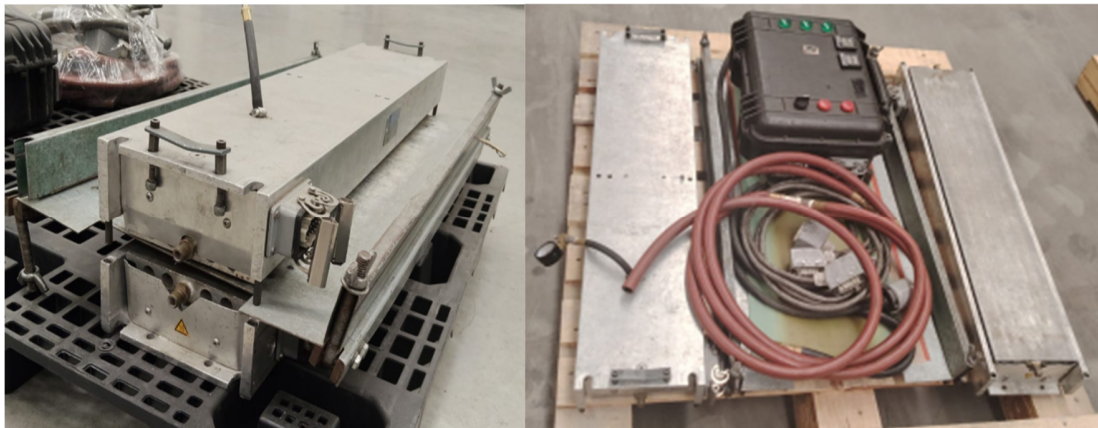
Prensa Ammeraal Beltech (Conjunto de Emenda)
